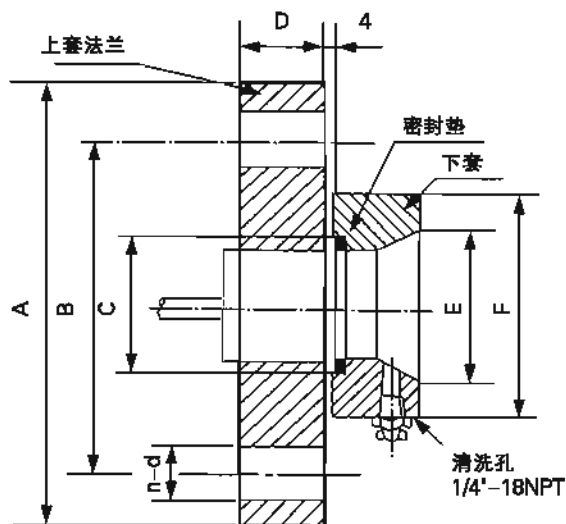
1199RFW 型法兰安装远传装置 (外形尺寸)
